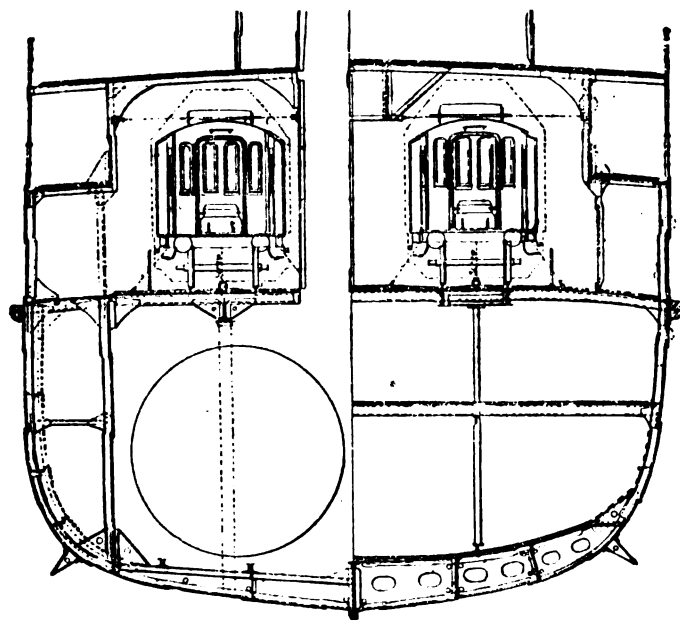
Ferry-boat delle Ferrovie Svedesi - Sezione trasversale.
